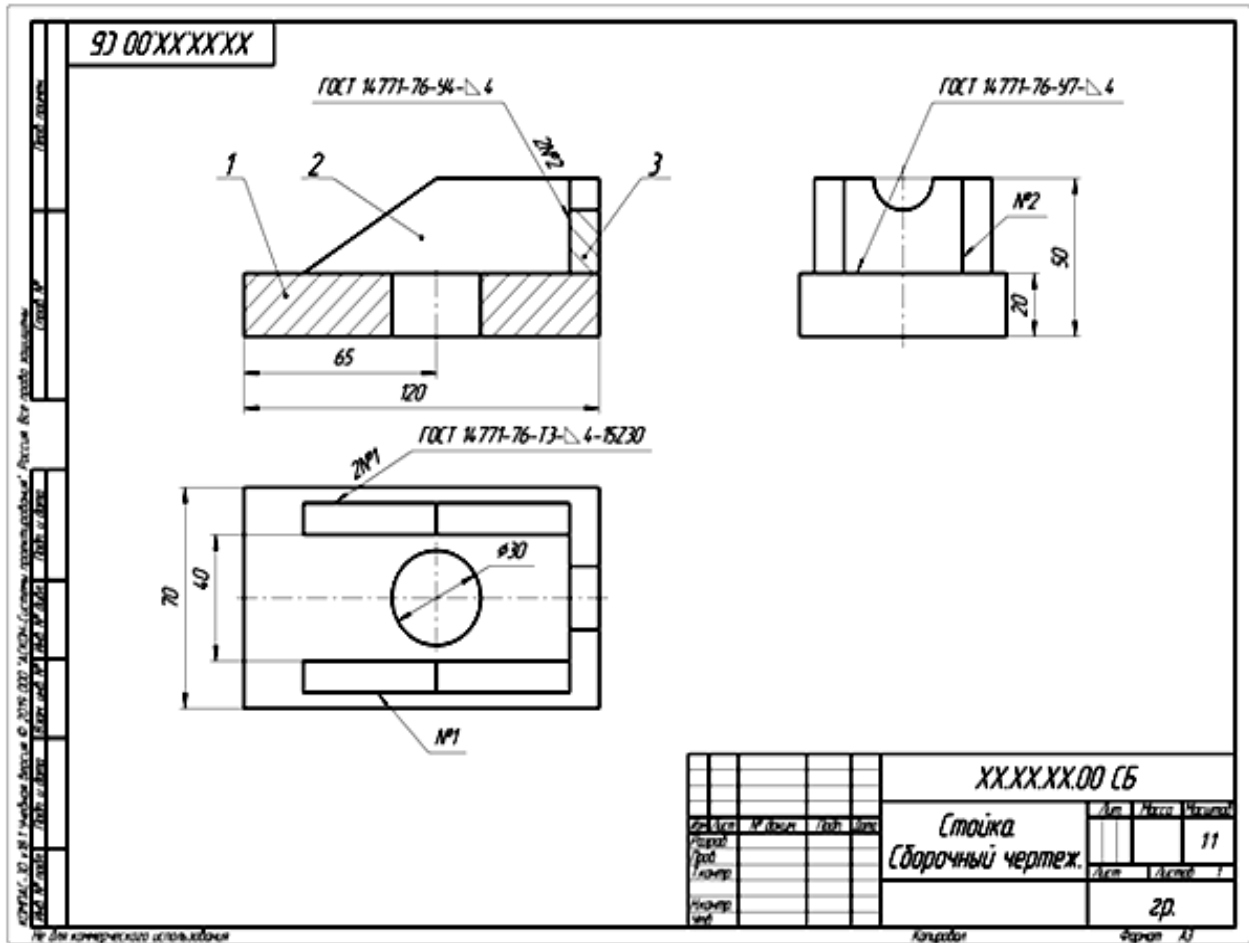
Пример выполнения сварного соединения
